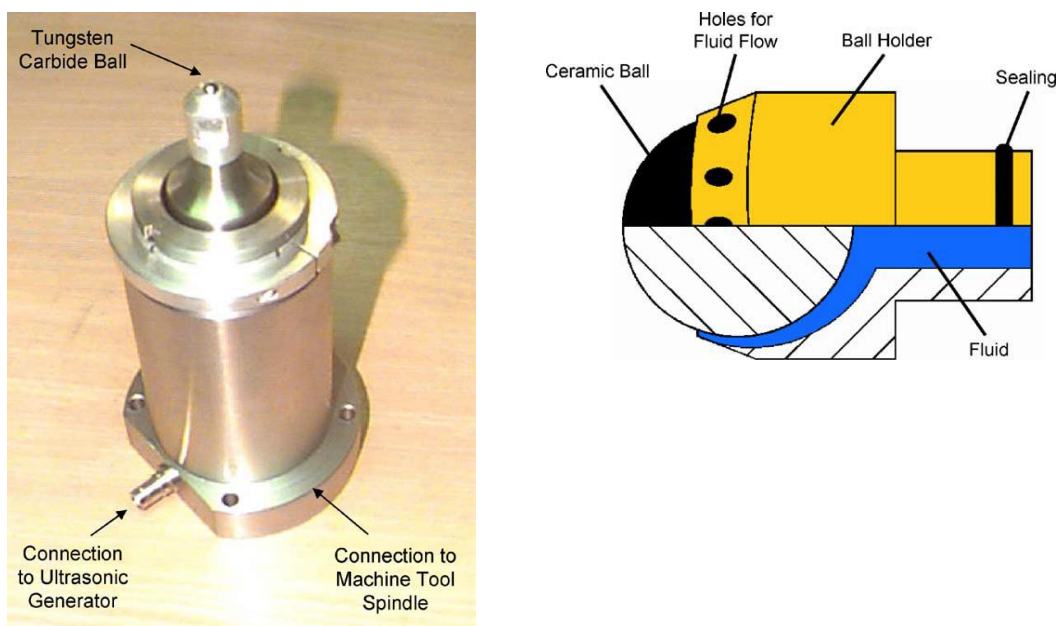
Конструкция устройства для ультразвуковой упрочняющей обработки фирмы Ecoroll (Германия)
